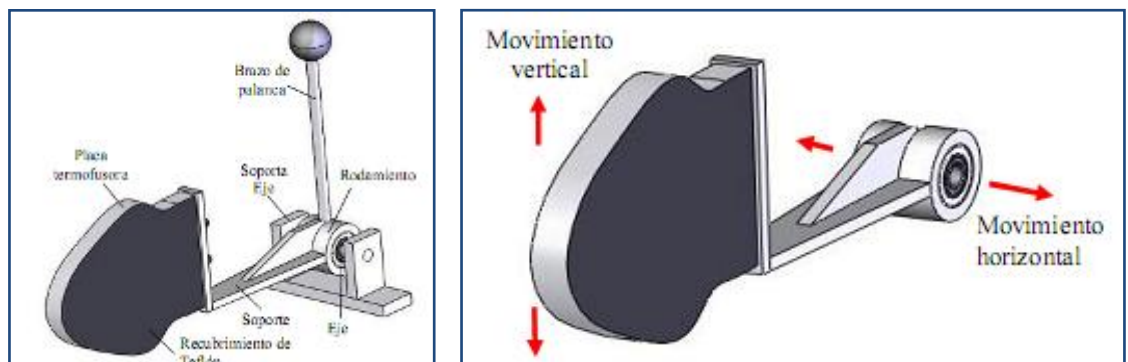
Despiece de máquina soldadora de termoplásticos.
